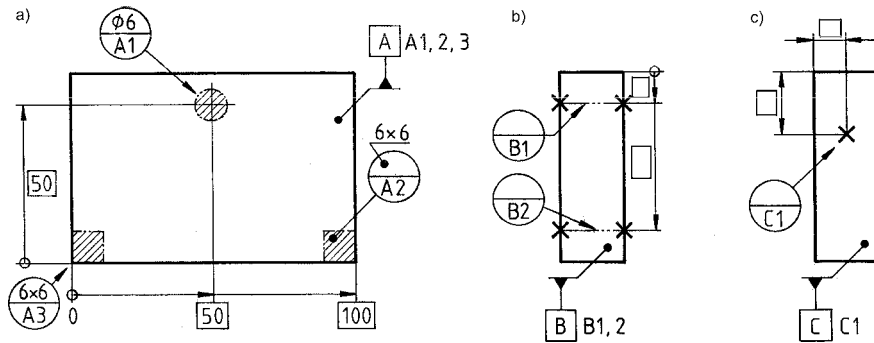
Möglichkeiten zur Bezugsstellenangabe. a) Flächenauflage an 3 Bezugsstellen, b) Linienauflage an 2 Linien, c) Punktauflage an 1 Punkt
